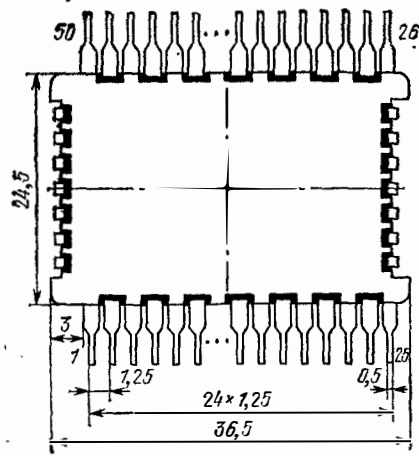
Конструкция керамического корпуса 421.50-1
